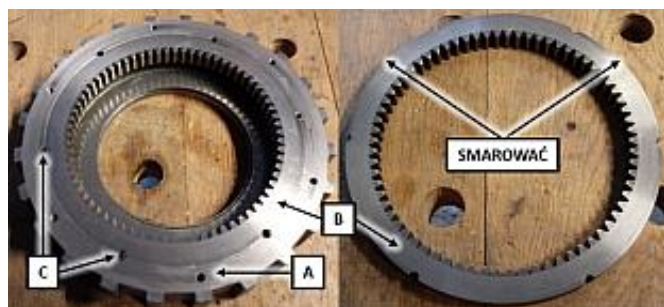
Montaż łożyska wzdłużnego w zespole koła zewnętrznego
